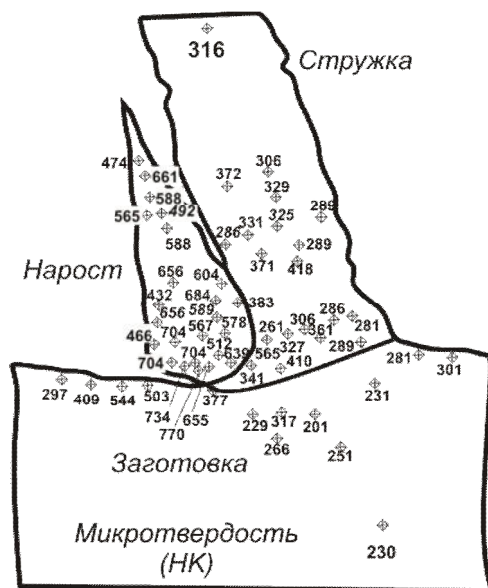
Микротвердость нароста, стружки и заготовки [45]
